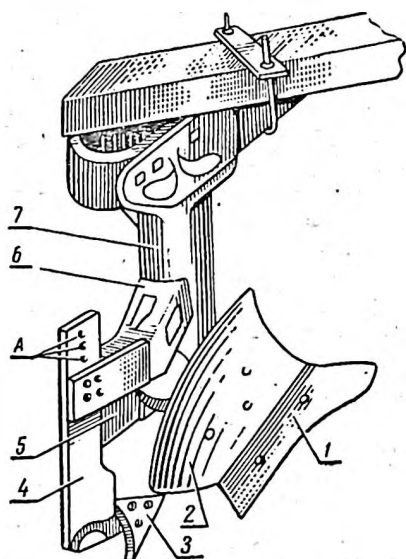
Схема корпуса плуга ПВП-4-35; 1 — лемех; 2 — отвал; 3 — лапа почвоуглубителя; 4 — стойка почвоуглубителя; 5 — полевая доска; 6 — кронштейн; 7 — стойка корпуса.
